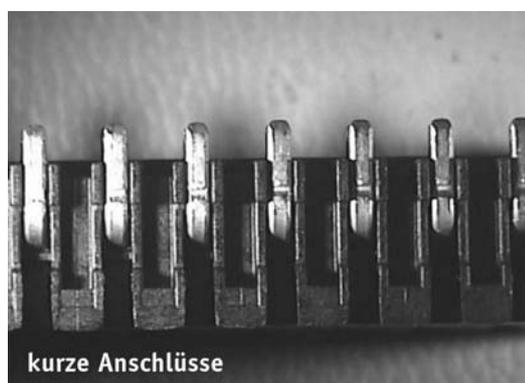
Beispiel für die untersuchten Steckerbauteile
